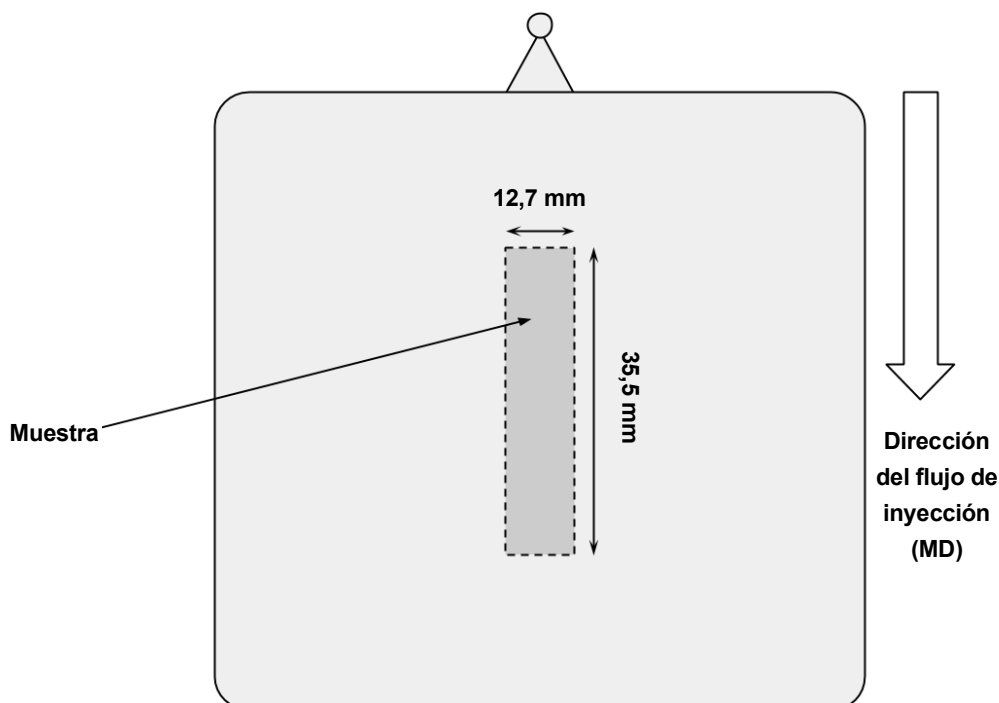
Esquema de una de las placas inyectadas detallando la zona de obtención y las dimensiones de las probetas para los ensayos DMTA.
